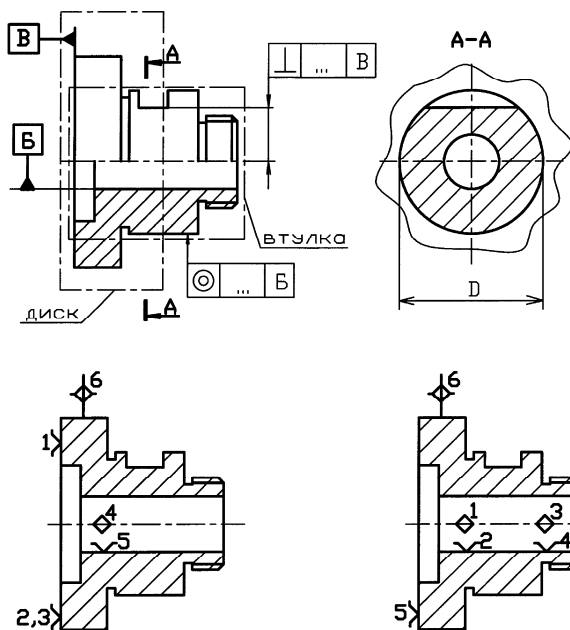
Базирование заготовки с элементами диска и втулки
